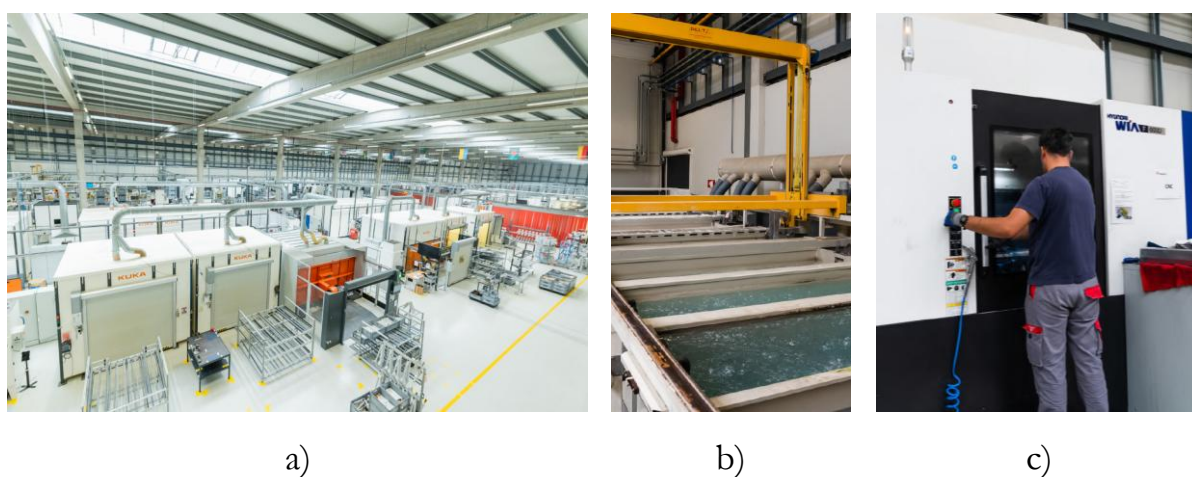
Exemplos de naves de produção da *Triangle's*: a) Soldadura robotizada; b) Lavagem; c) Maquinação CNC
